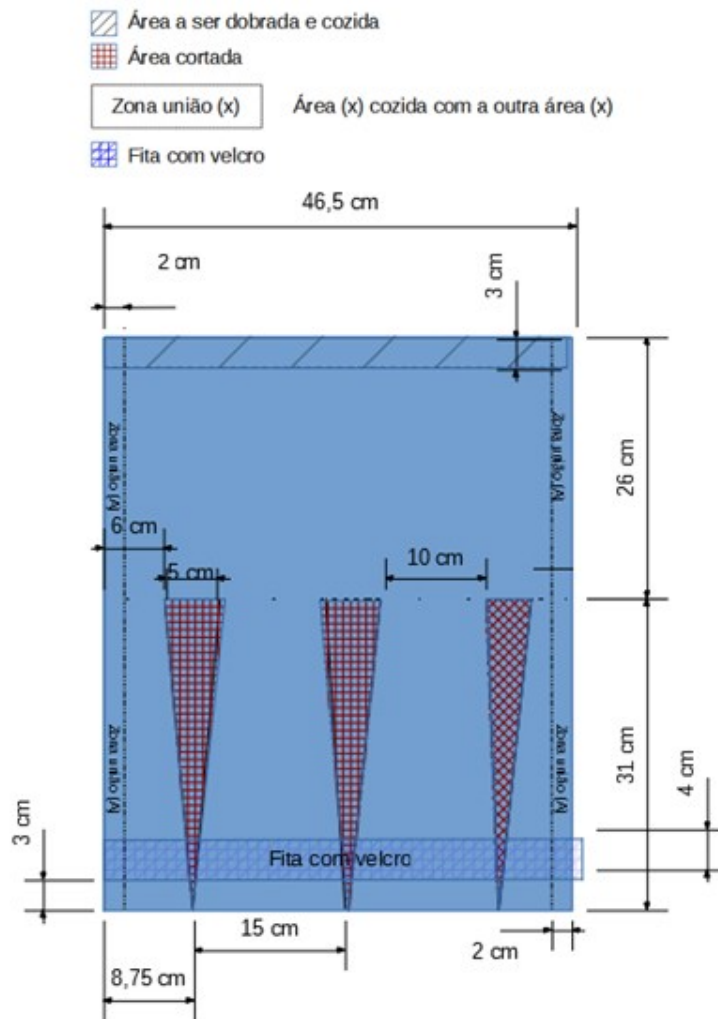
Dimensões e esquema de corte da capa de proteção.
